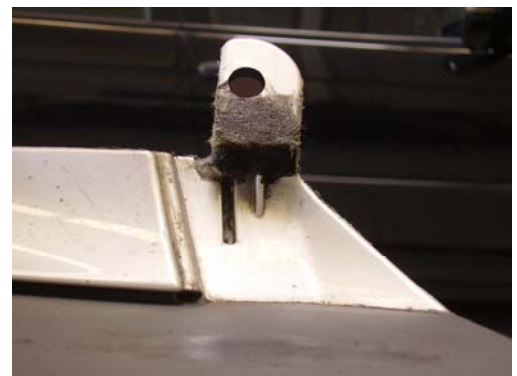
Beidseitig verschweißte Befestigungslasche
